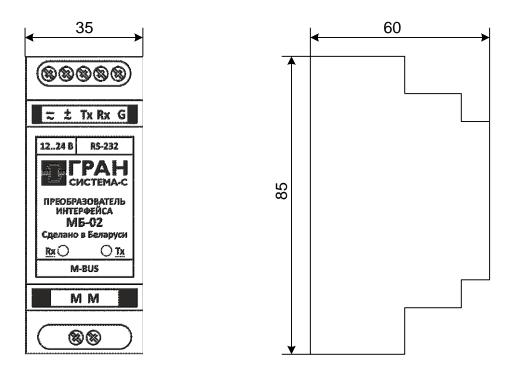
Габаритные размеры преобразователя «МБ-02»
